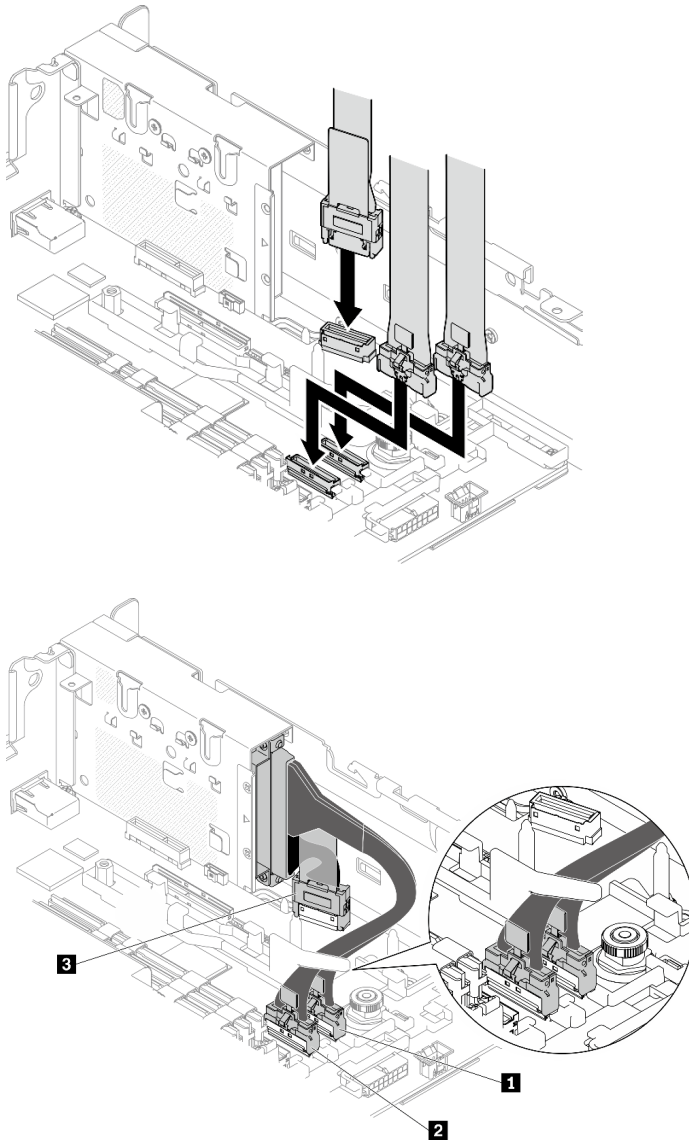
Disposición de los cables para el adaptador OCP 3.0 Ethernet
